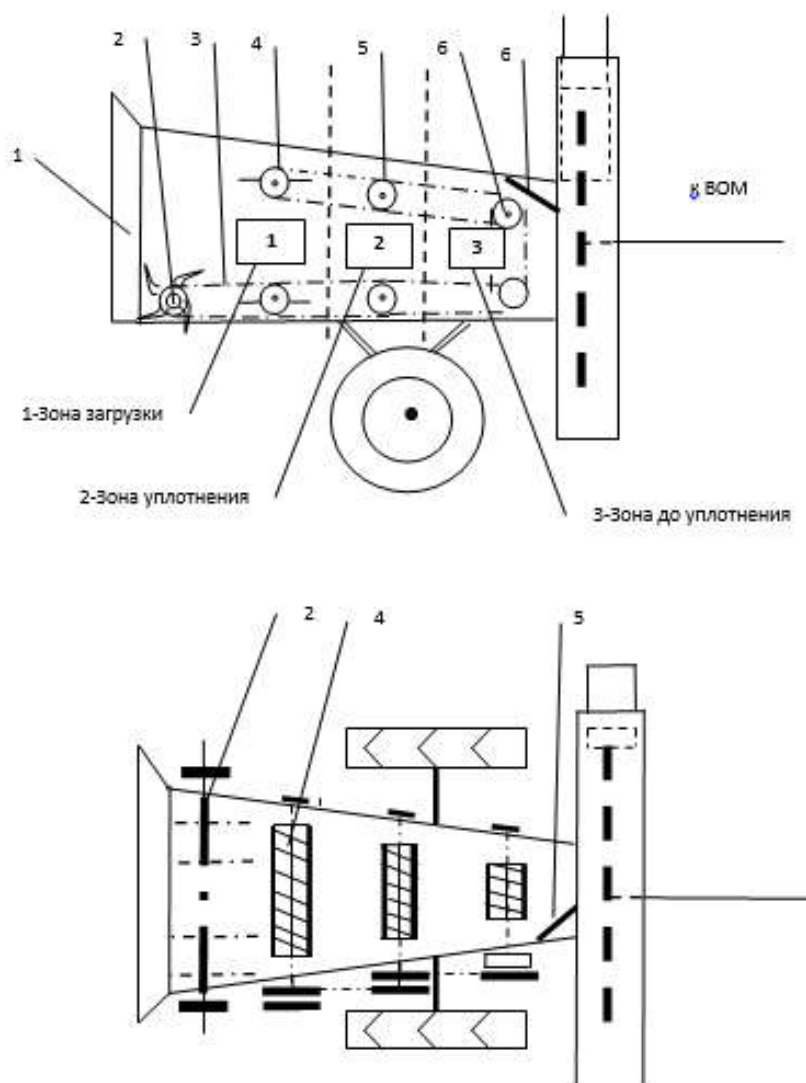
Схема механизма подачи устройства для измельчения порубочных остатков
